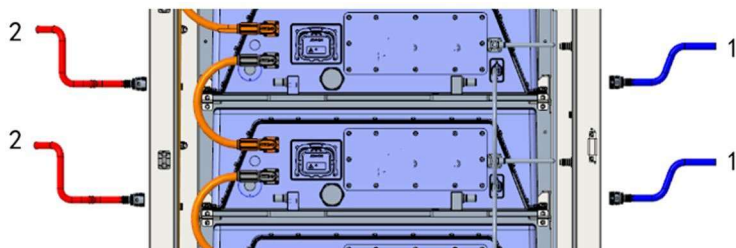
Retirada de la tubería de refrigerante
